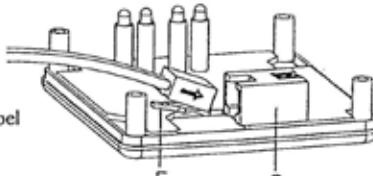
Rumsgivaren inifrån och montering av motorns kabel
